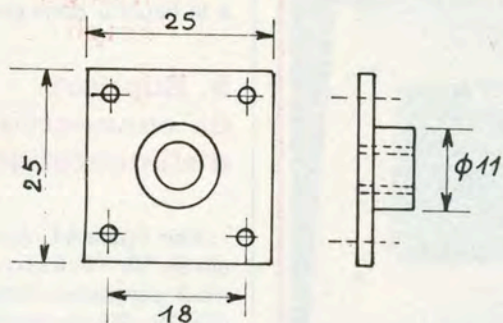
Pièce de support. Ecrou central taraudé à 5 soudé ou brasé.
